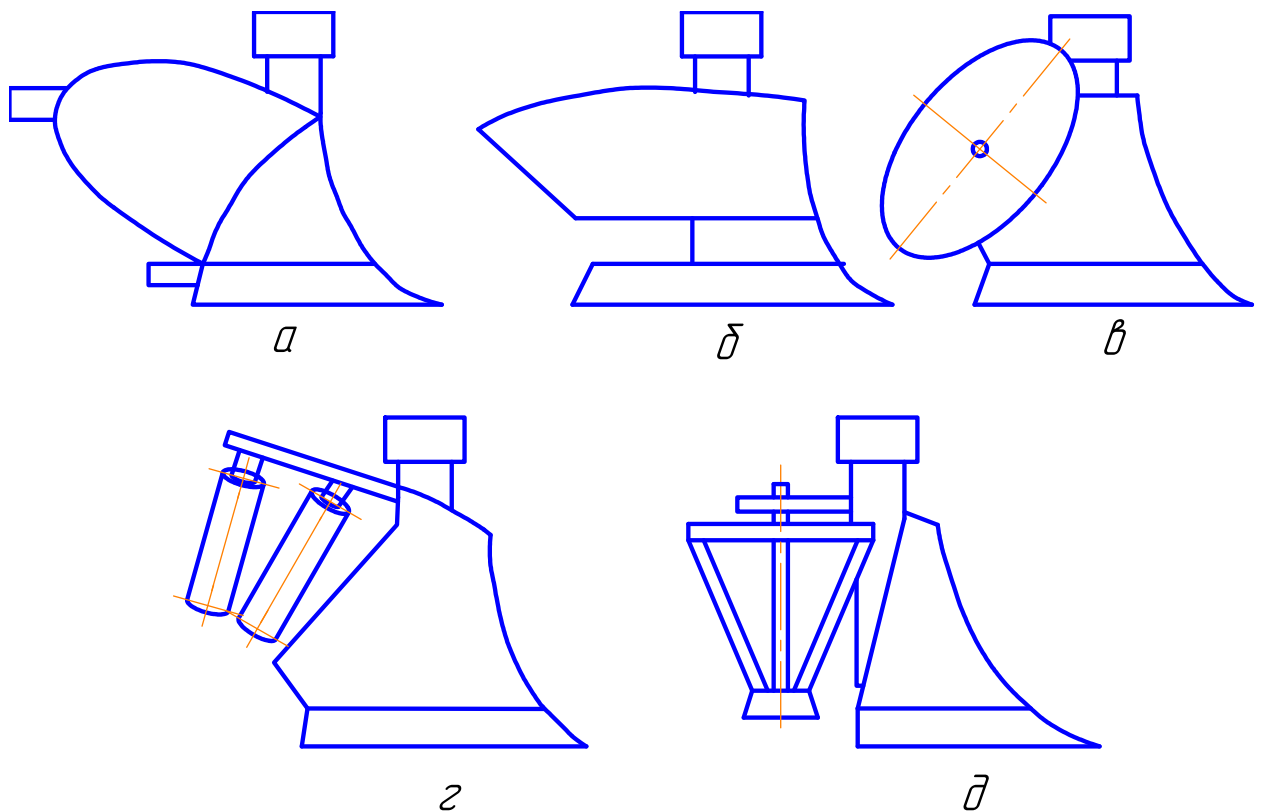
Корпуси плугів з різними типами полицевих поверхонь:
